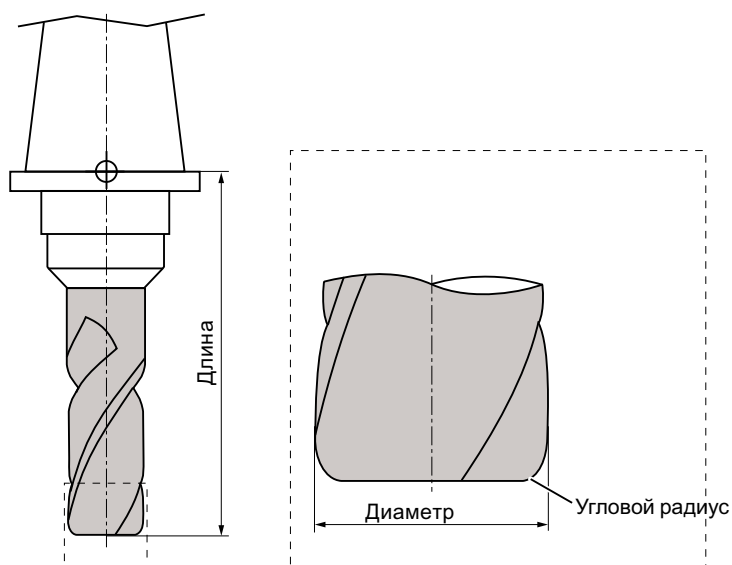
Инструмент 3D на примере концевой фрезы с закруглением углов (тип 121)
